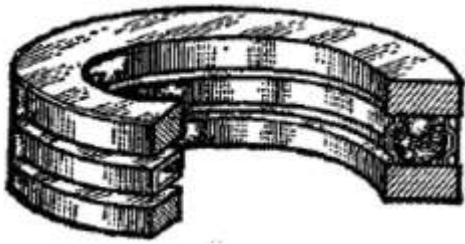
Упорные шарикоподшипники Рис. 2.87. Двойной упорный шарикоподшипник
